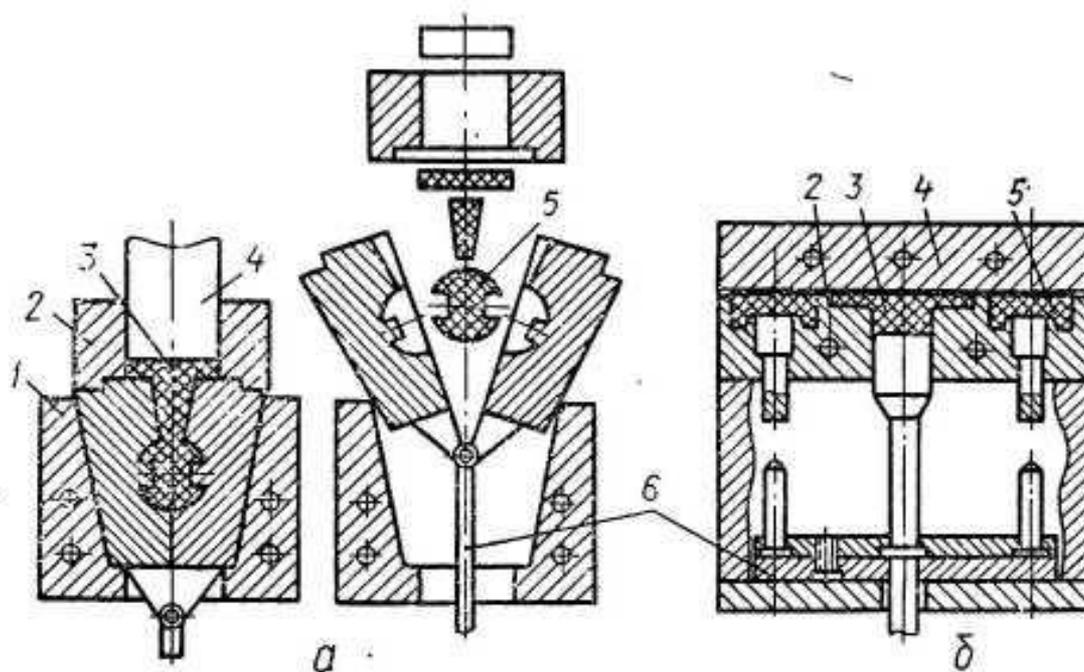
Пресс-формы для литьевого прессования с верхней (а) и нижней (б) загрузочной камерой: 1 – корпус; 2 – матрицы; 3 – загрузочная камера; 4 – пуансон; 5 – изделие; 6 – выталкивающая система
